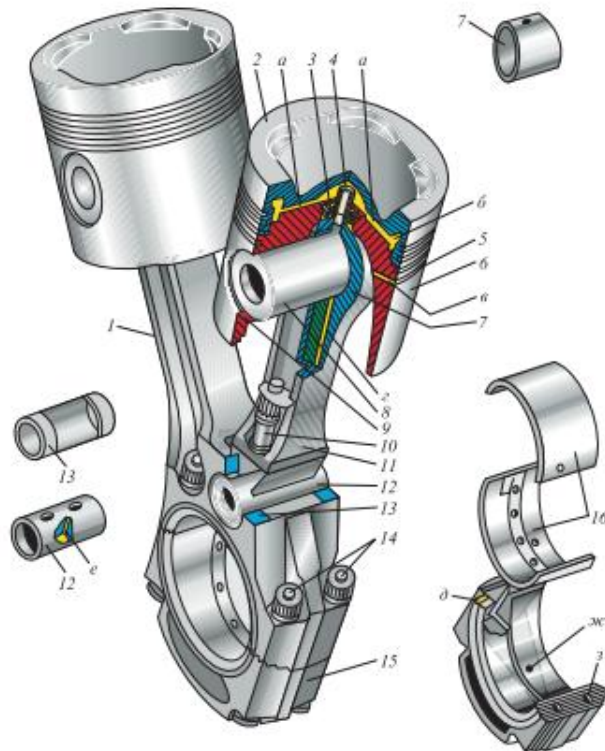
Кривошипно-шатунный механизм: 1 — главный шатун; 2 — поршень; 3 — пружина; 4 — стакан; 5 — маслосъемное кольцо с экспандером; 6 — тронк; 7 — втулка верхней головки шатуна; 8 — палец; 9 — стопорное кольцо; 10 — болт прицепного шатуна; 11 — прицепной шатун; 12 — палец прицепного шатуна; 13 — втулка-подшипник; 14 — шатунные болты; 15 — крышка; 16 — вкладыши; о, в, г, д, е — каналы; б — полость охлаждения; ж — отверстие под штифт; з — зубчатый стык
